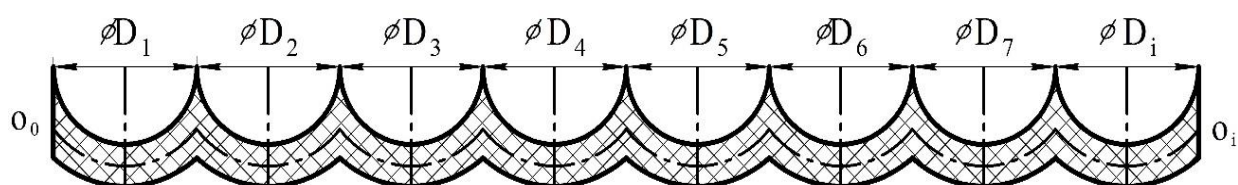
Переріз частини корінцевої клейової полімерної пластини книжкового блоку зшитого нитками
